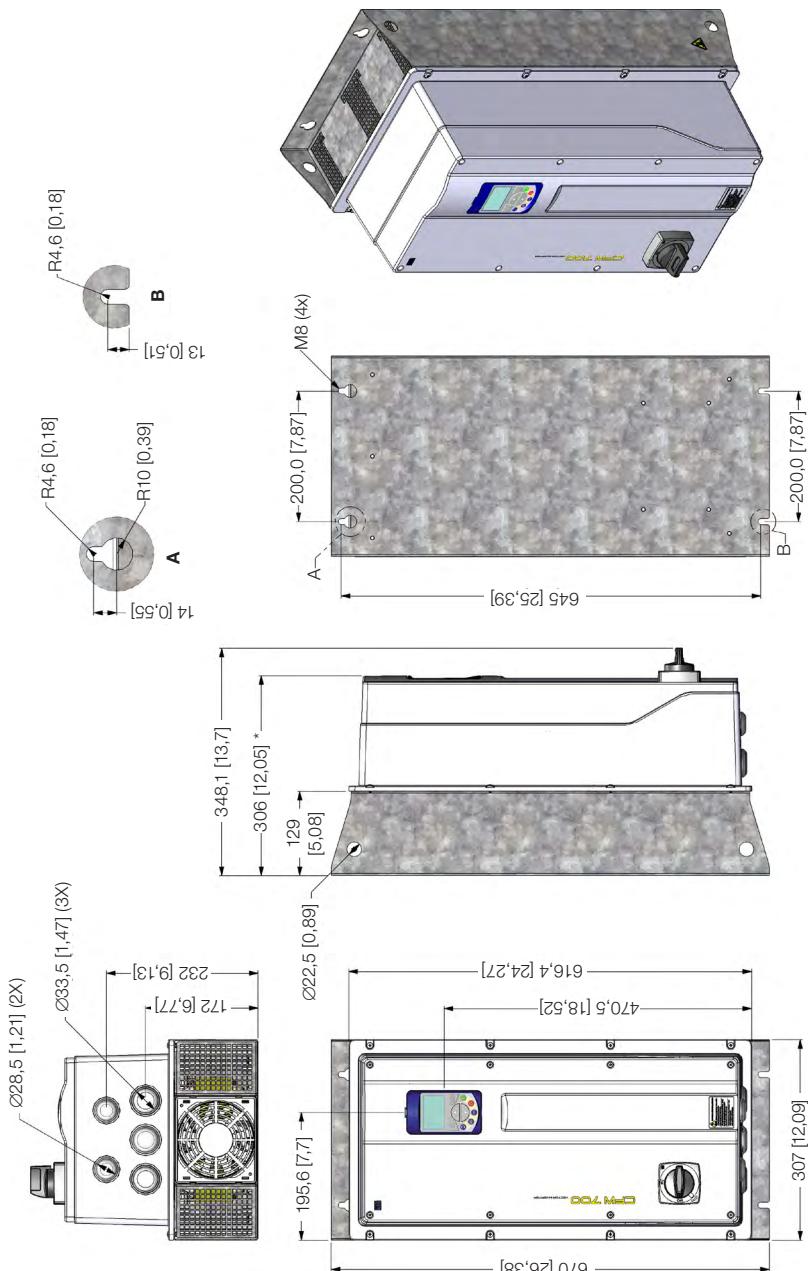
Wechselrichterdimensionen in mm [in] - rahmengröße C mit schutzgrad IP54
